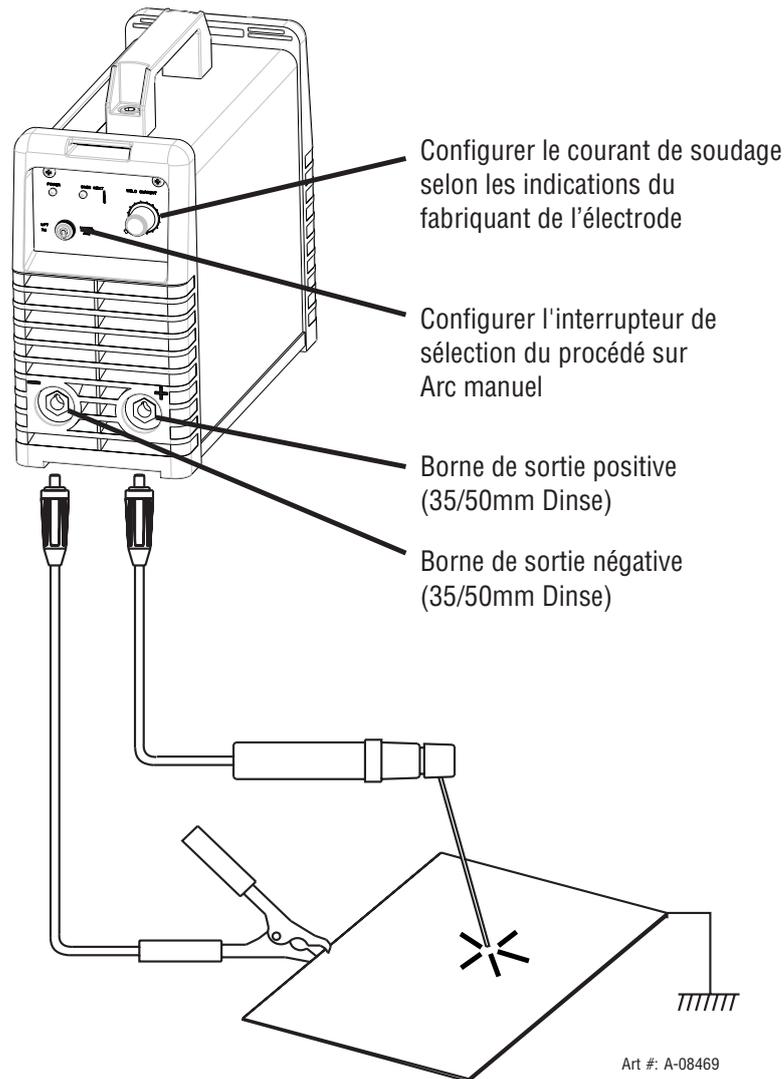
Configuration pour le soudage à l'arc manuel (STICK)
